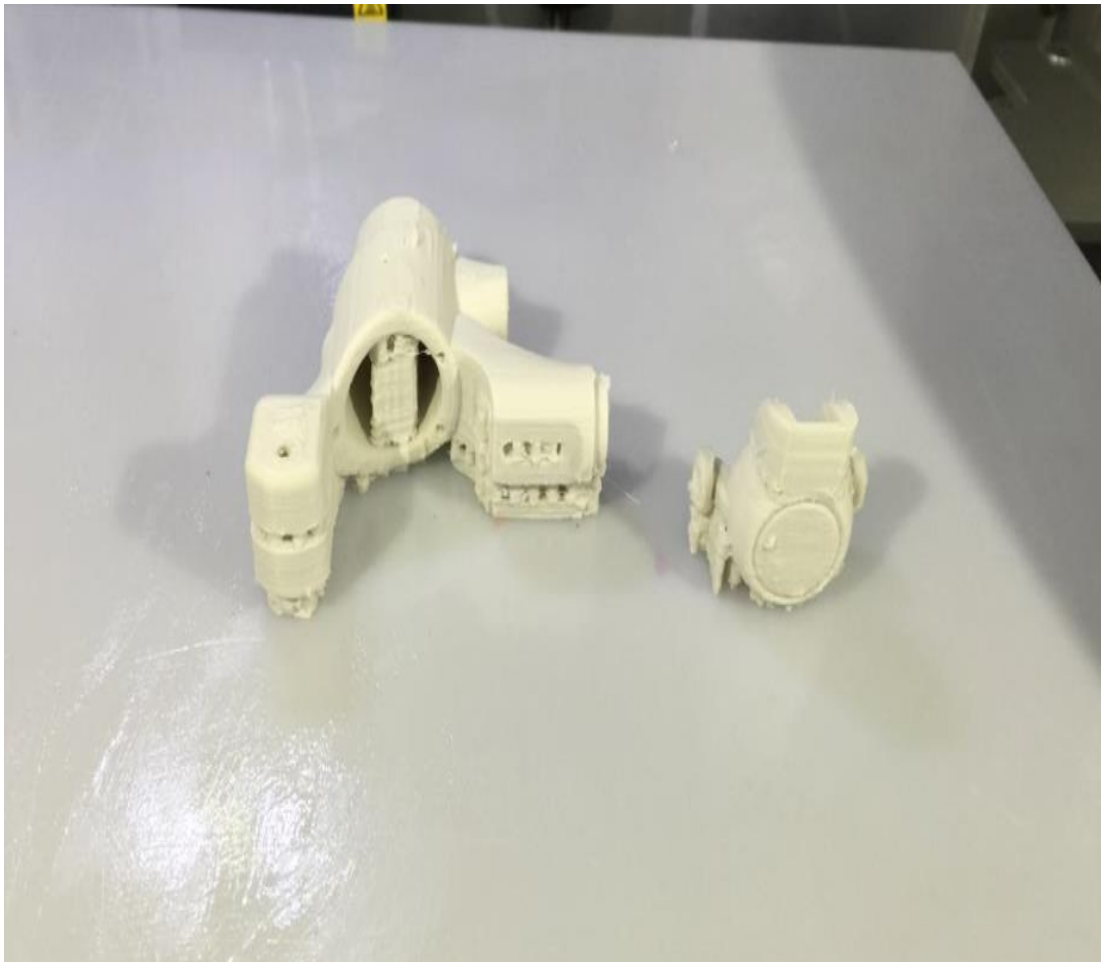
Impresión 3D de piezas para máquina para tatuajes
